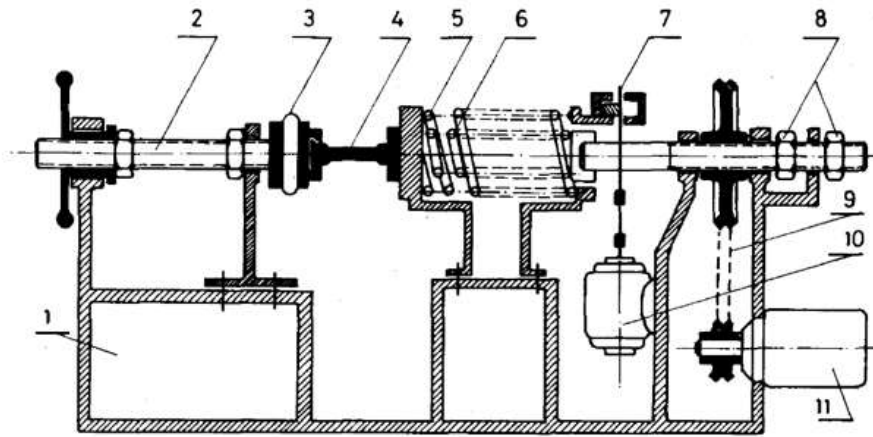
Disposición constructiva máquina de ensayos de fatiga axial Schenck (Galal S., 1990)
